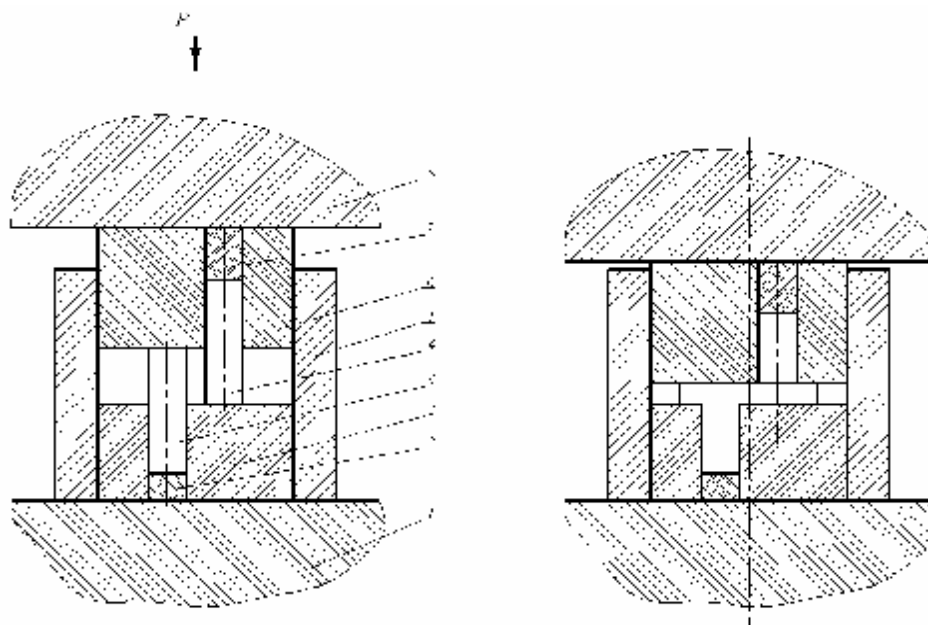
Схема одновременной высадки двух цилиндрических заготовок
